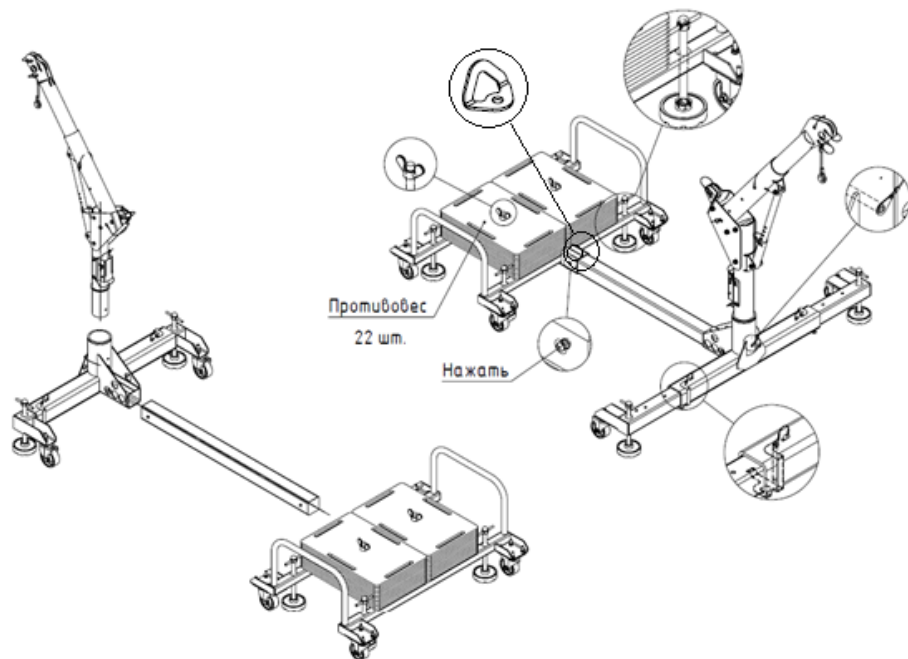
Монтаж СОБ Кран Е11-4L
